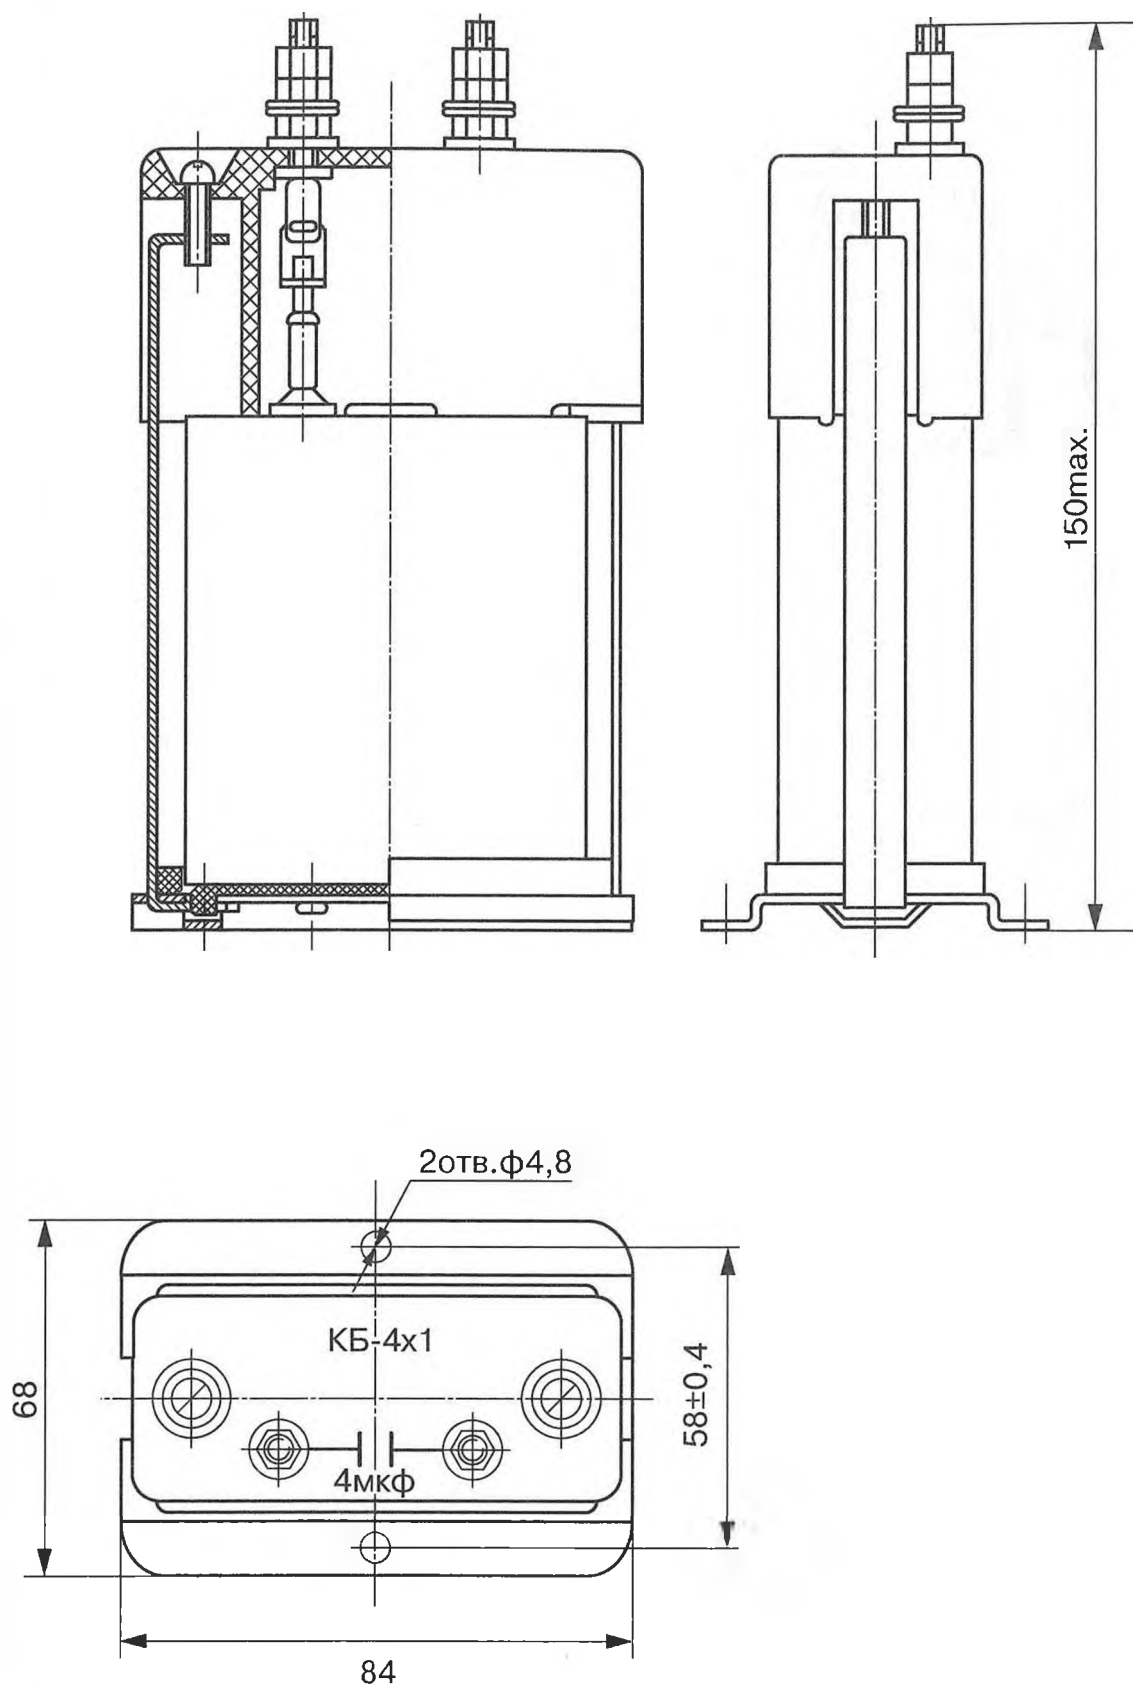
Габаритные и установочные размеры блока конденсаторного KB-4x1
